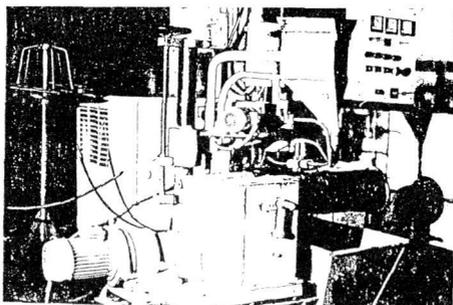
Общий вид станка СРМ-051 для электродуговой наплавки деталей машин в ультразвуковом поле
